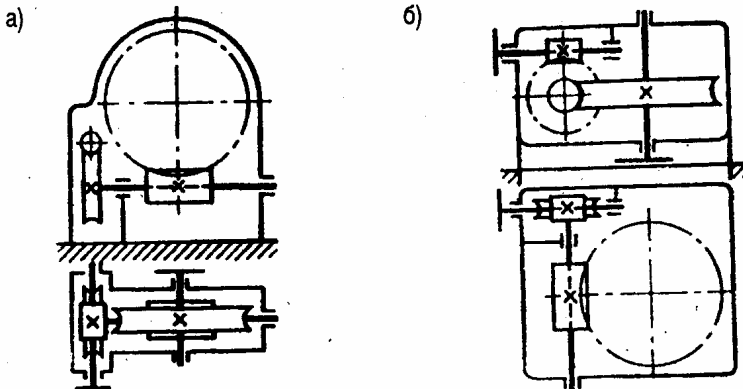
Кинематические схемы червячных двухступенчатых редукторов:
